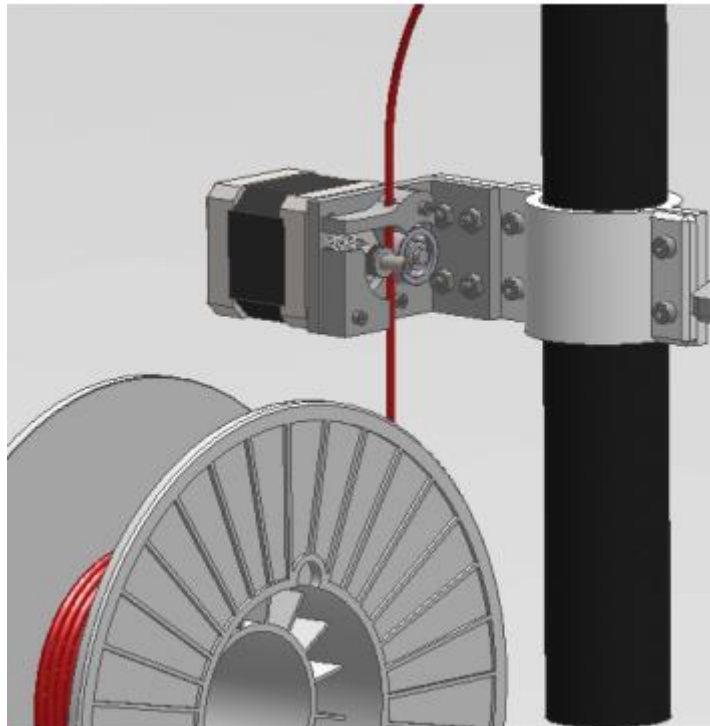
Rolo de filamento e sistema de movimentação com motor e cilindros em pinçamento
